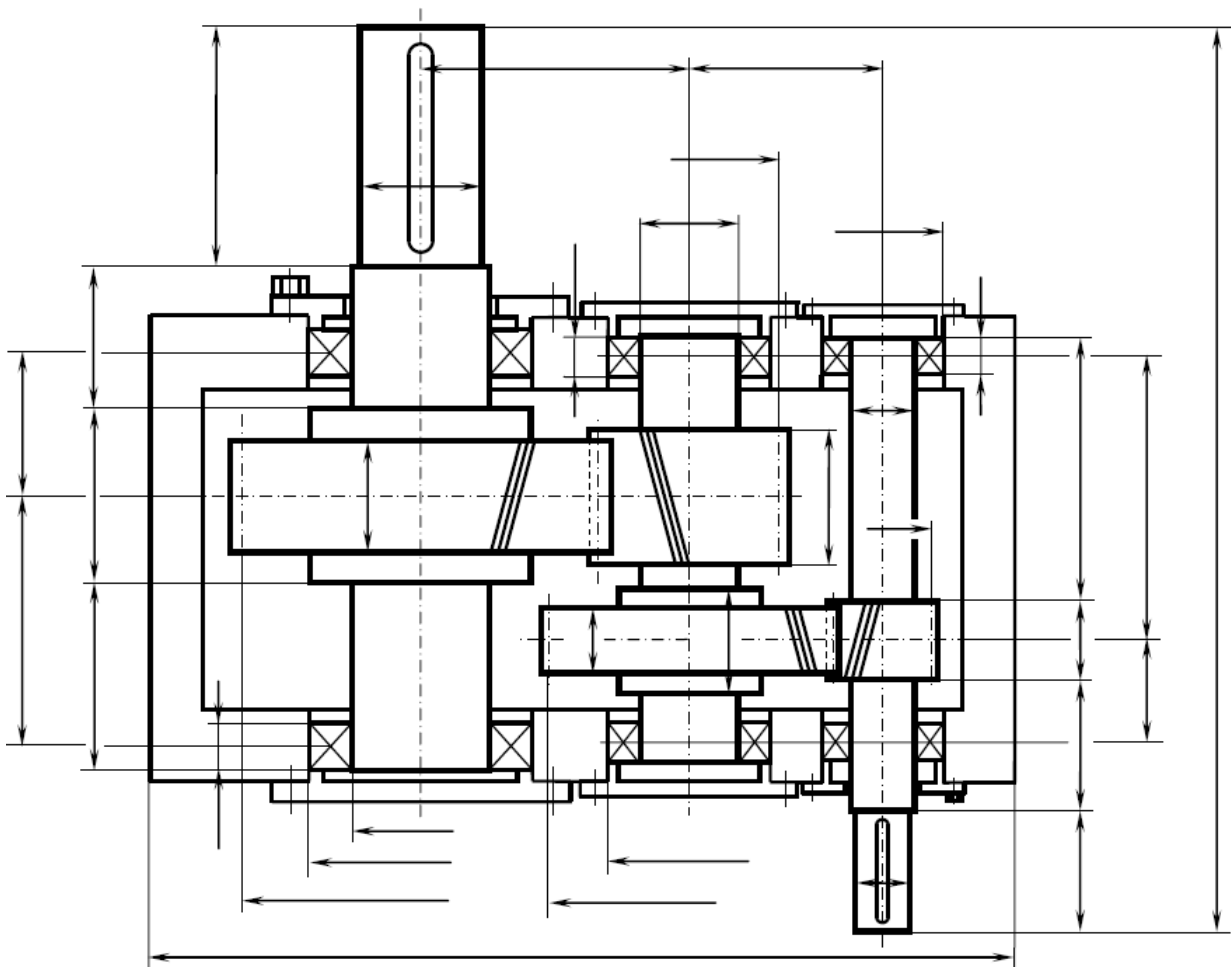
Эскиз компоновки двухступенчатого горизонтального цилиндрического редуктора
